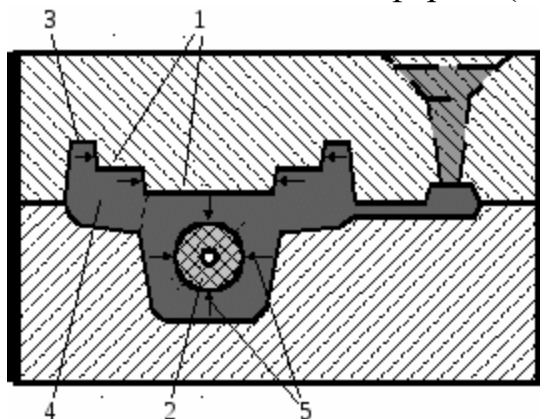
Схема возникновения усадочных напряжений в отливке корпуса: 1 – выступающие части формы; 2 – стержень; 3 – опорная ножка корпуса; 4 – утолщение опорной части корпуса; 5 – сжимающие усадочные напряжения
